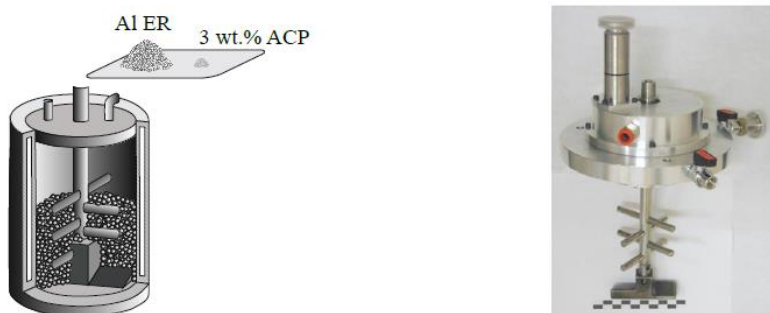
Esquema de molino attritor (izquierda) y tapadera modificada (derecha)
